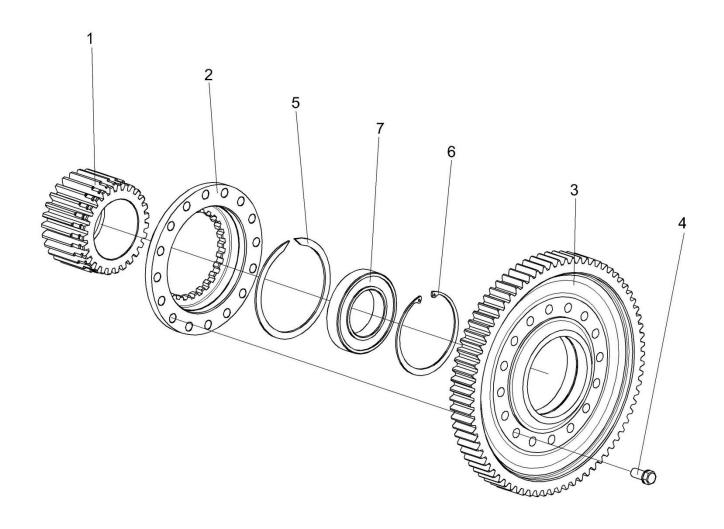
Колесо зубчатое МК-23М.03.210
